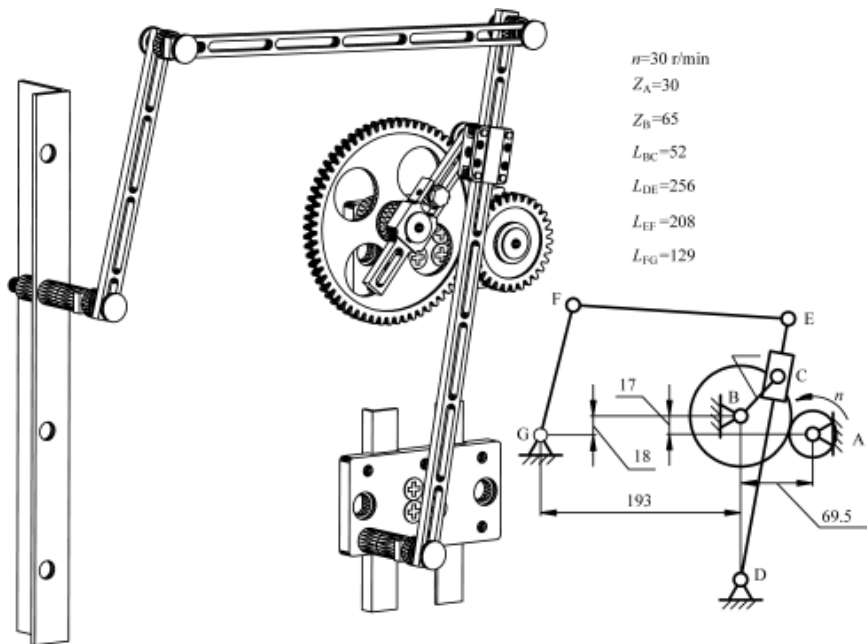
机构 6（齿轮——六杆）的运动简图、参数及实际组装
